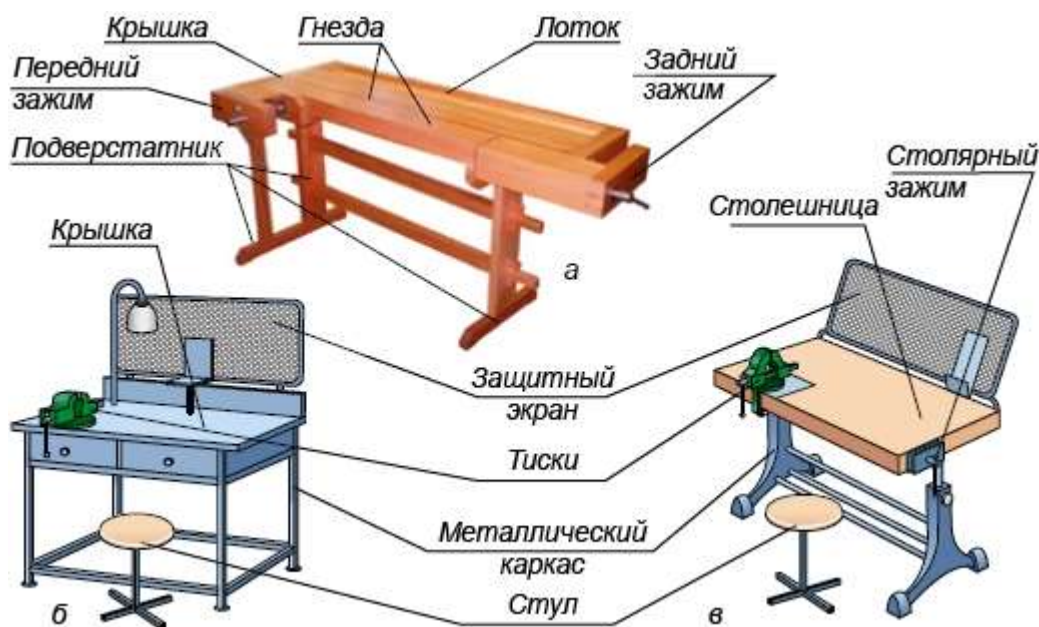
Верстаки: а – столярный; б – слесарный; в – комбинированный
